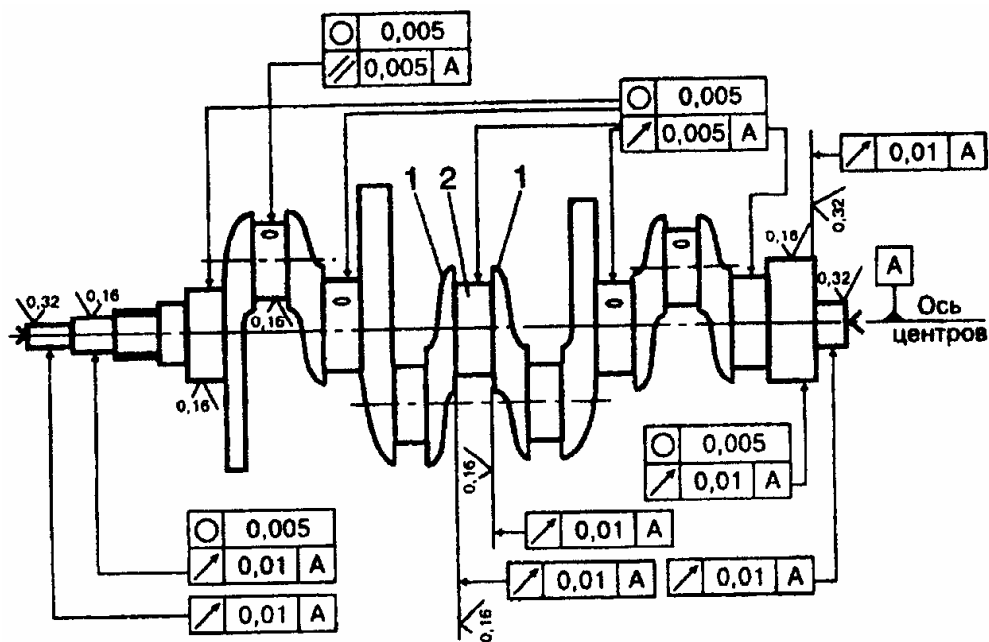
Схема и основные требования к качеству и расположению поверхностей коленчатого вала: 1 – щека, 2 – шейка
